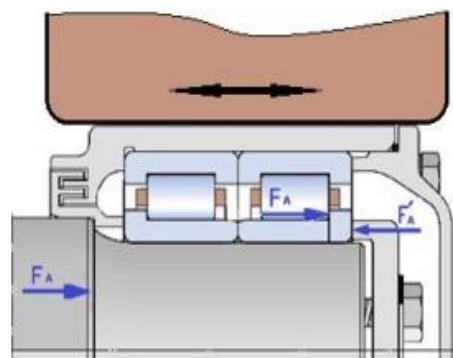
Схема передачі осьового навантаження в буксовому вузлі з циліндричними підшипниками
